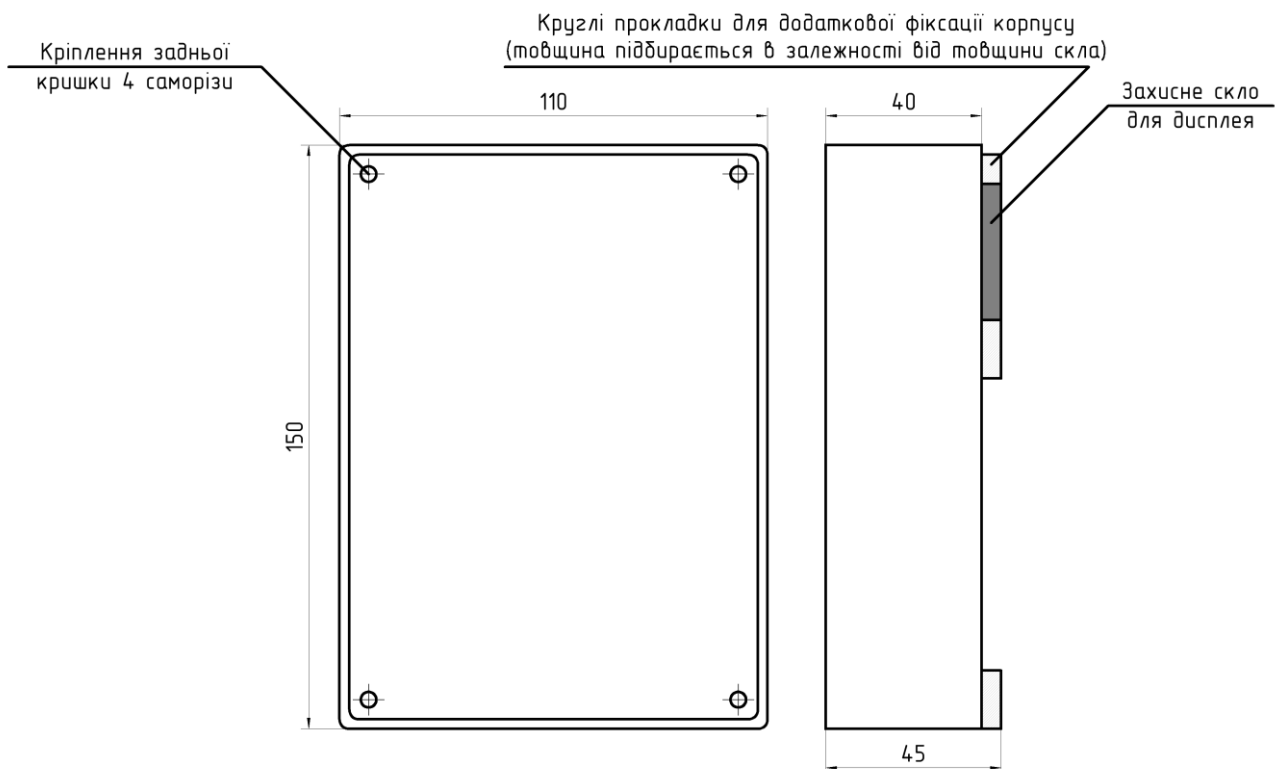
Зовнішнє компонування корпусу пристрою
